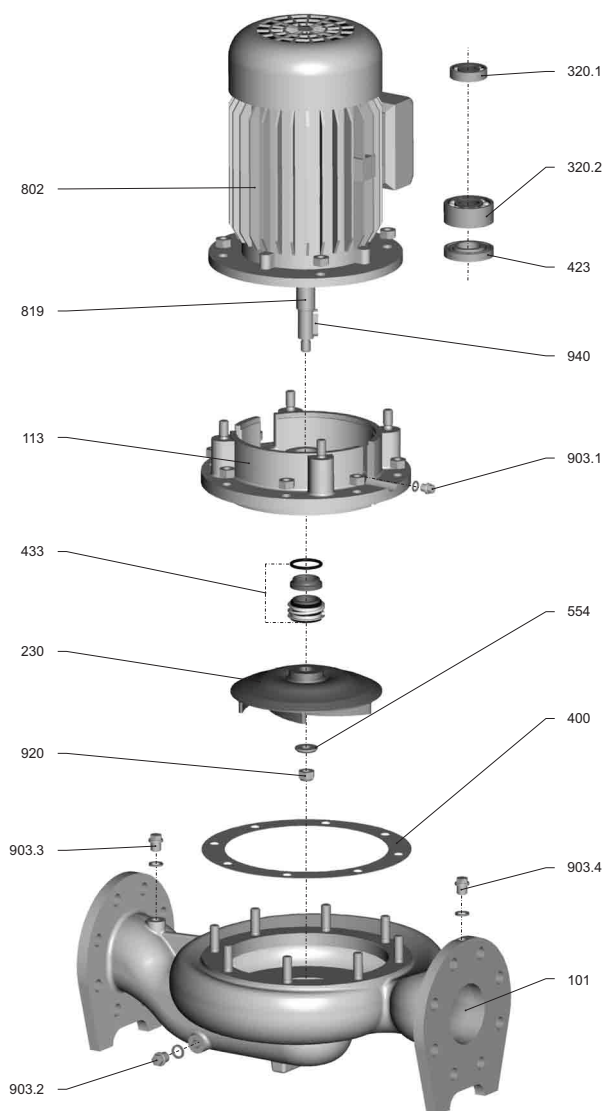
Rysunek w rozłożeniu na części (wersja konstrukcyjna GFC)
